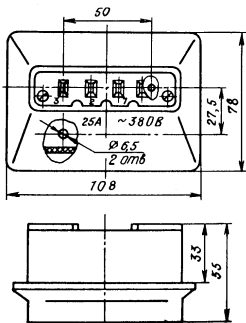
Габаритные, установочные размеры розетки прямоугольной формы для скрытой установки
